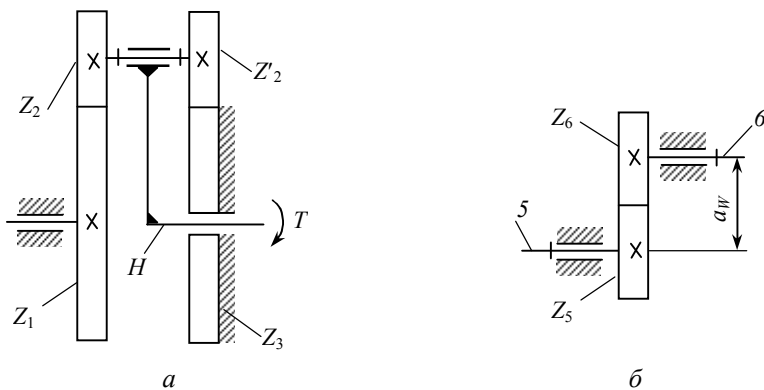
Редуктор (*a*) и механизм привода контура каскада радиоустройства (*б*)
